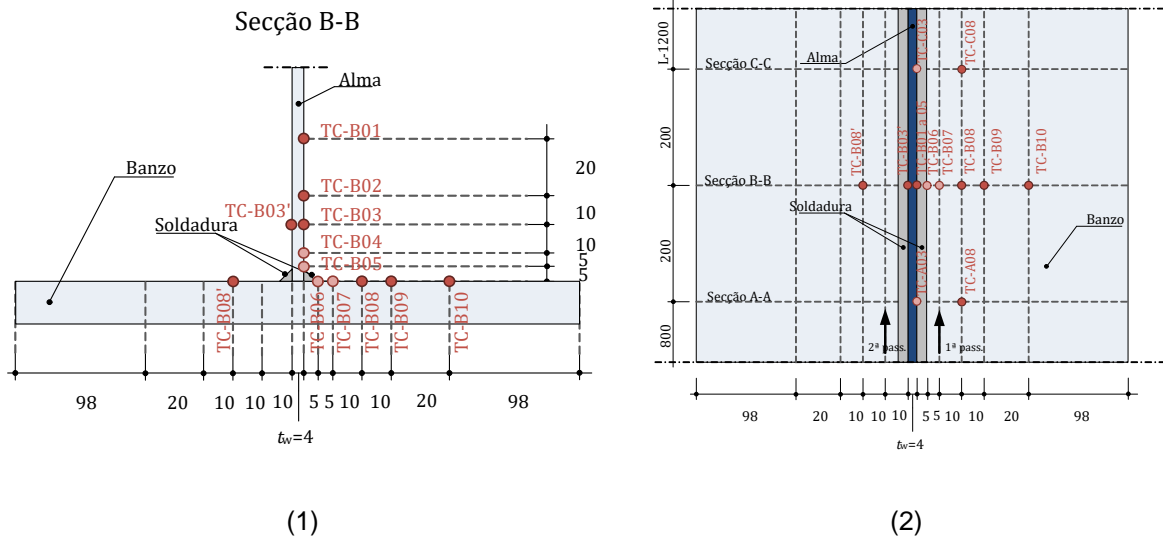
Localização dos termopares nas vigas do grupo A: (1) visão em corte, (2) visão em planta (Dimensões em milímetros)
